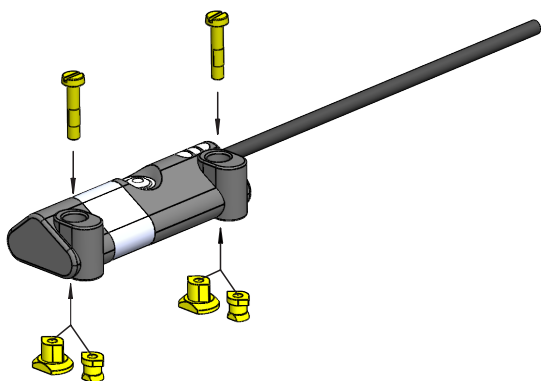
Montagem dos fixadores de ranhura T (lado esquerdo) ou fixadores de ranhura C (lado direito)
